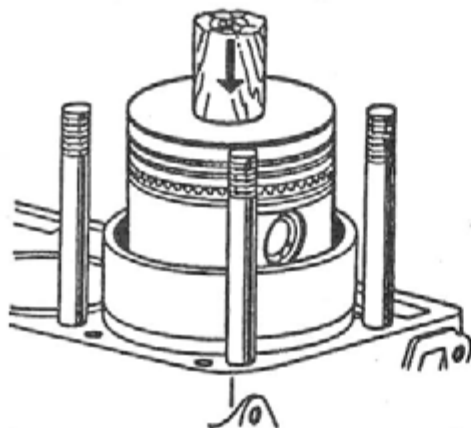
Установка поршня с кольцами в цилиндр с помощью приспособления 5-У-11106
